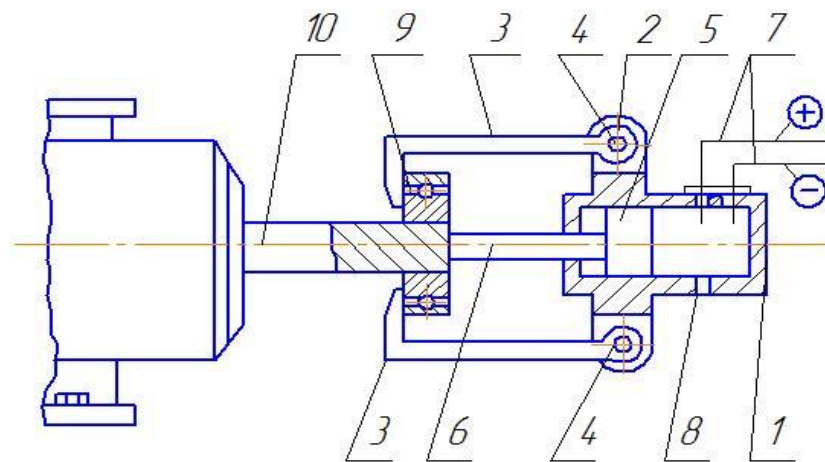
Пристрій для демонтажу підшипників з валів: 1 – корпус; 2 – вушка; 3 – захоплювачі; 4 – фіксуючі болти; 5 – поршень; 6 – силовий шток; 7 – електроди; 8 – штуцер; 9 – деталь, що знімається; 10 – вал.
